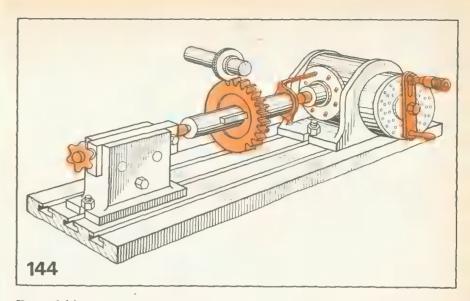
Прием фрезерования впадин зубьев модульного колеса
